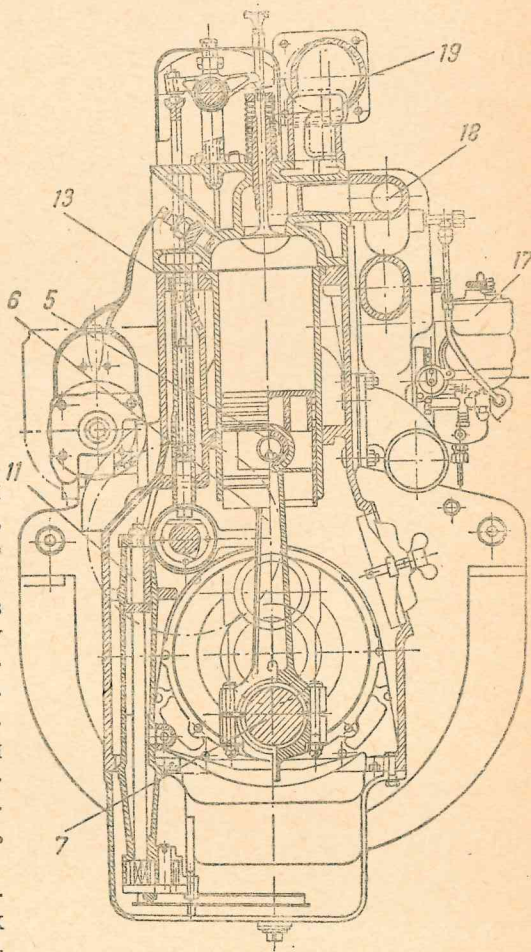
Двигатель СТЗ—ХТЗ (поперечный разрез)
